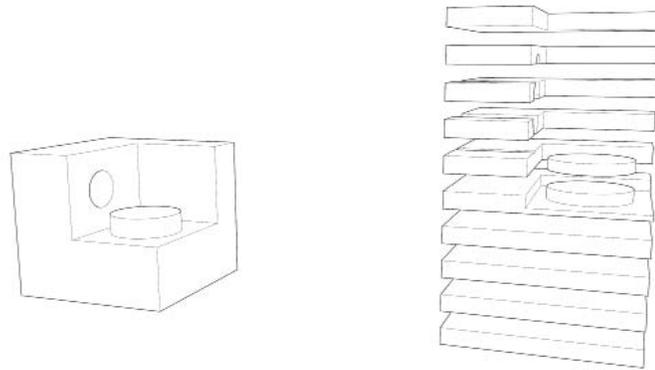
Modelo CAD (izquierda) y modelo separado en capas para impresión 3D (derecha).
